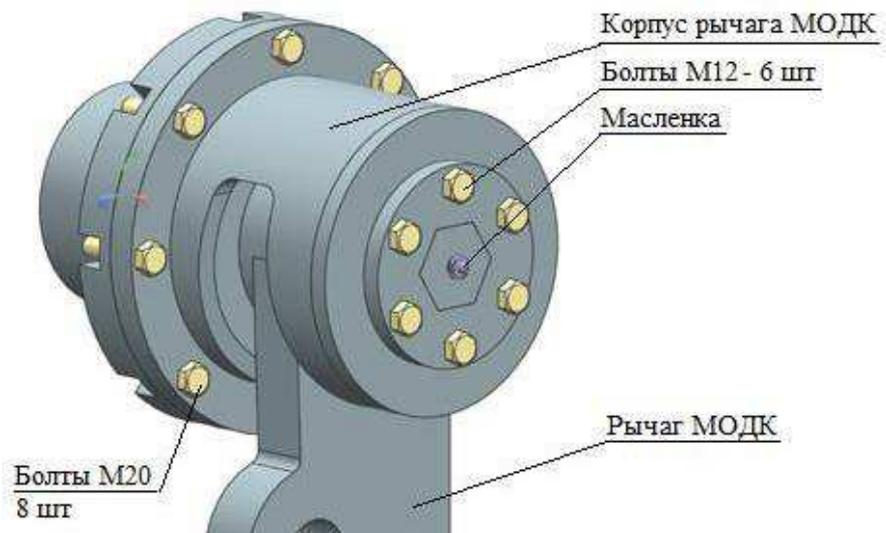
Укрупнённый вид рычага и корпуса МОДК
